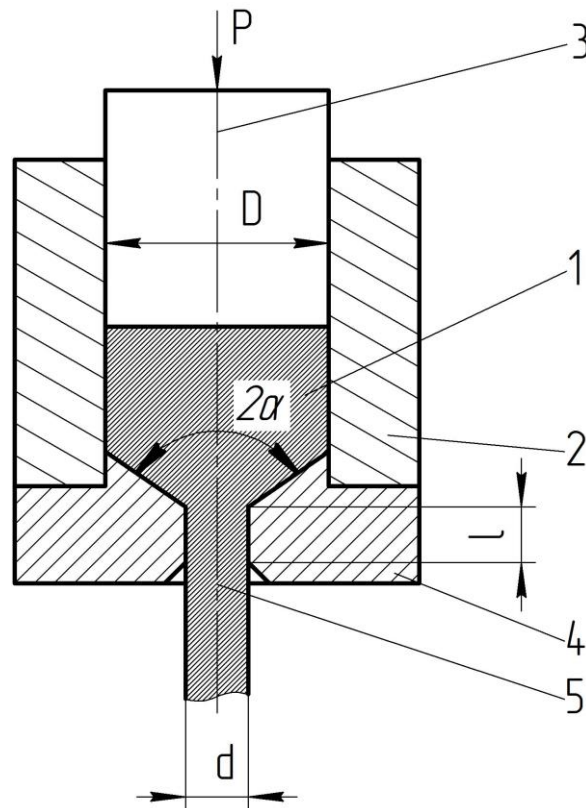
Схема процесу пресування : 1 – метал; 2 – контейнер; 3 – пуансон; 4 – матриця; 5 – виріб з металу.
